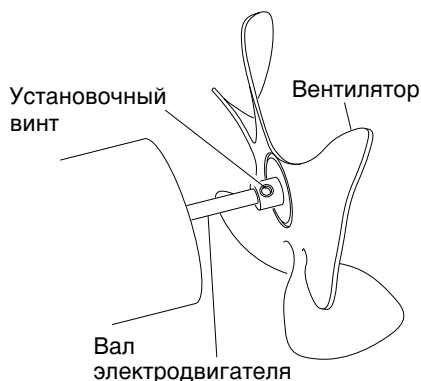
Расположение вентилятора, вала электродвигателя и установочного винта
